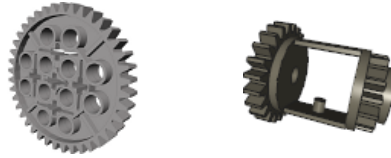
Engranajes utilizados en el eje trasero. A la izquierda el engranaje unido al motor (40 dientes) y a la derecha el diferencial unido al eje (24 dientes) (fuente: <http://sariel.pl>)
